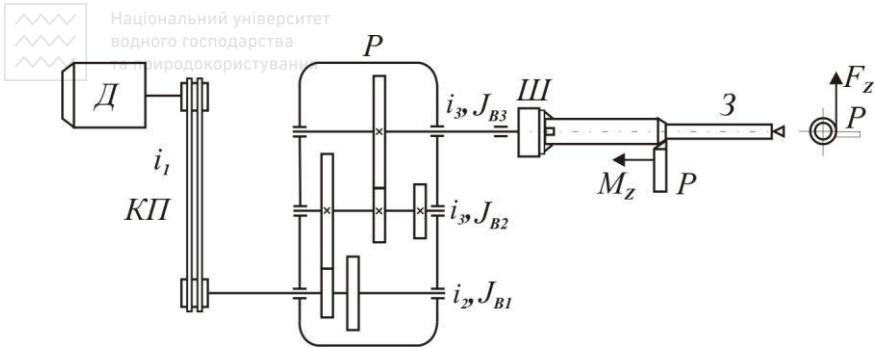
Кінематична схема привода шпинделя токарного верстата
